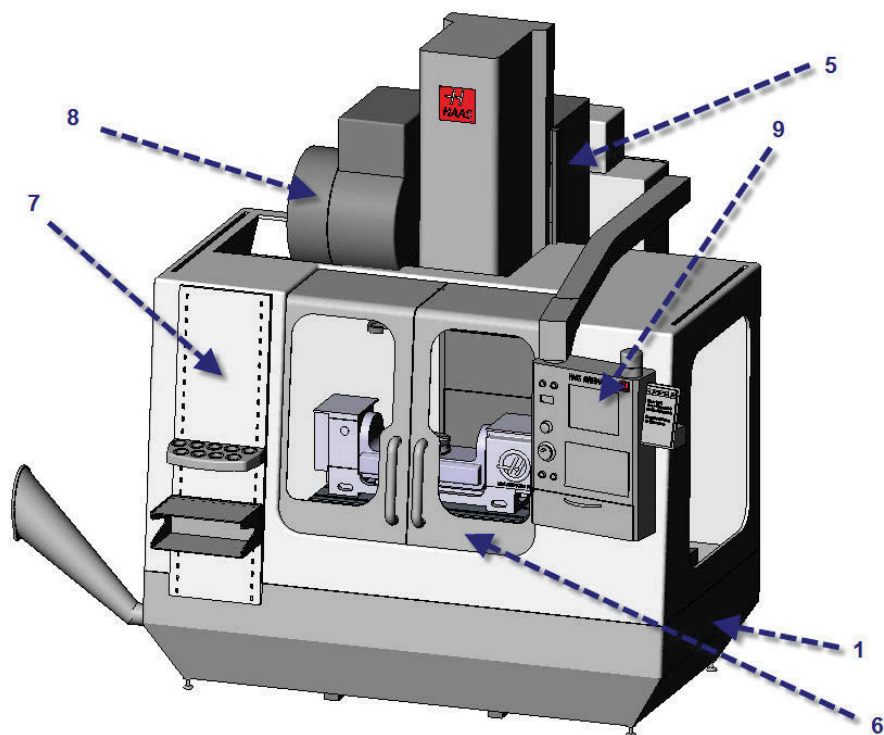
Корпус вертикально-фрезерного станка с ЧПУ
